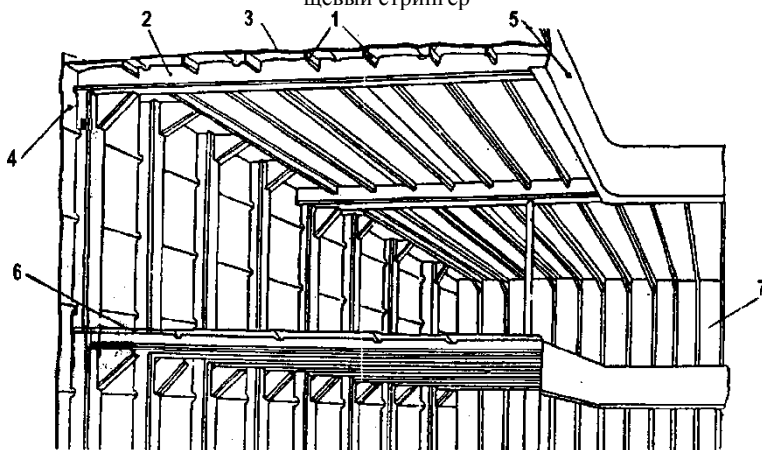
Конструкция перекрытия верхней палубы сухогрузного судна набранного по продольной системе:
